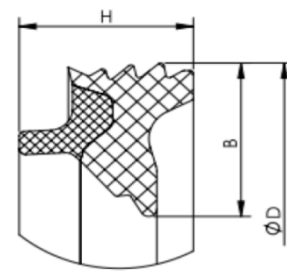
Garnitures d'étanchéité Solydo PP 10 du DN 125 au 400
